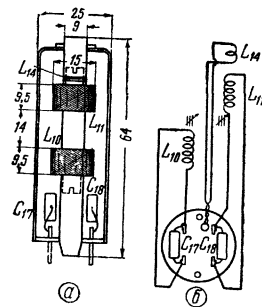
Полосовой фильтр: а — конструкция; б — схема соединения деталей
